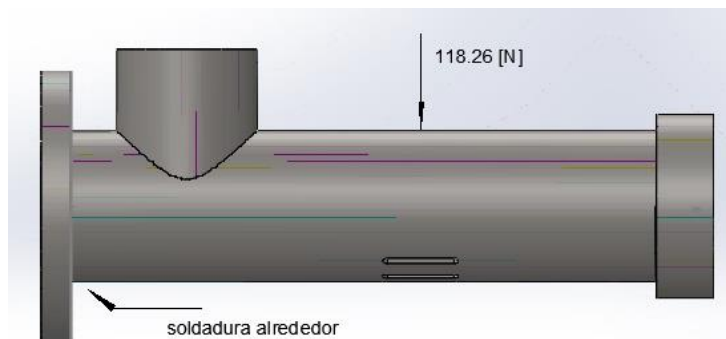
Diagrama estático del cordón de soldadura. Fuente: Autor
